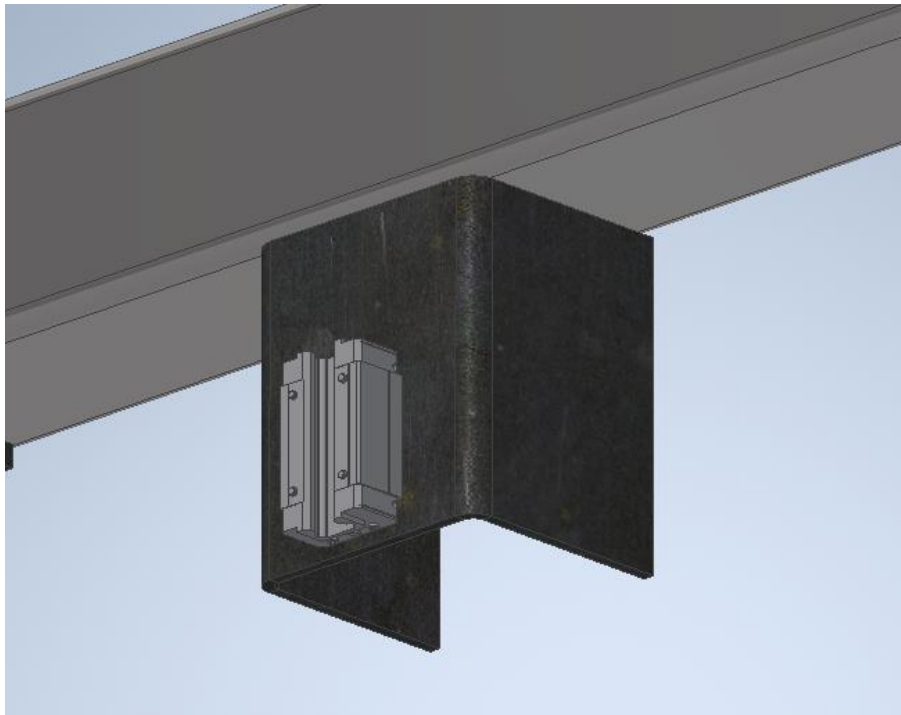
Detalle chapas soporte compuerta con patines para guía lineal.
